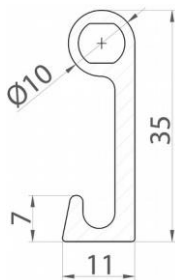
Профиль уплотнительный для установки по контуру откатных дверей
